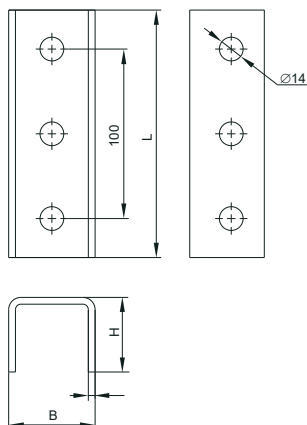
Крепление приварное для STRUT-профиля / Figure D.1 – Welded attachment for STRUT profile
